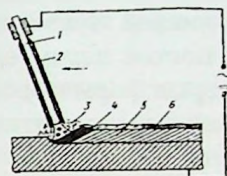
Схема поста для ручной дуговой сварки:
